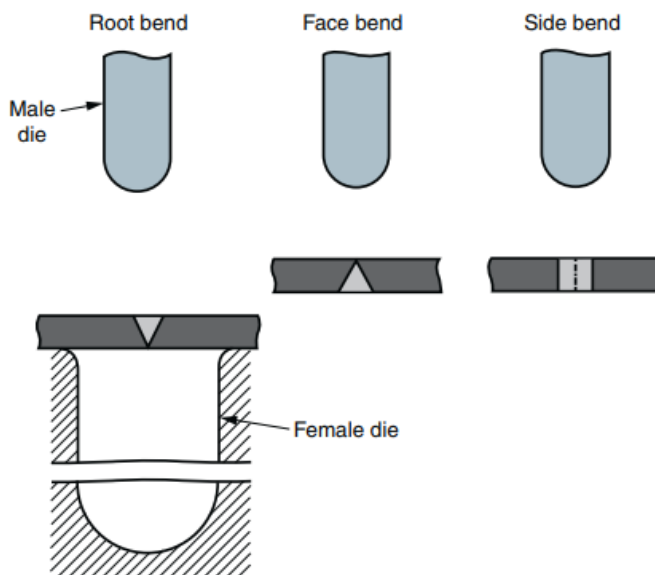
Los tres tipos de pruebas de flexión. La prueba de doblado lateral coloca la mayor cantidad de tensión a lo largo del eje de soldadura
